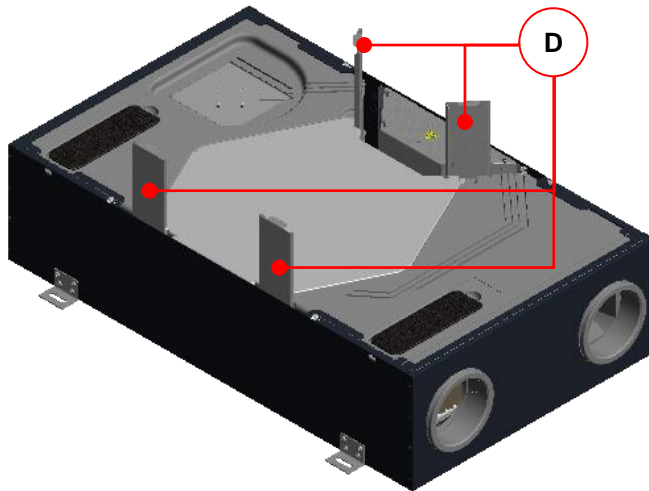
Halteklammern D zur formschlüssigen Fixierung der EPP-Schaummodule
